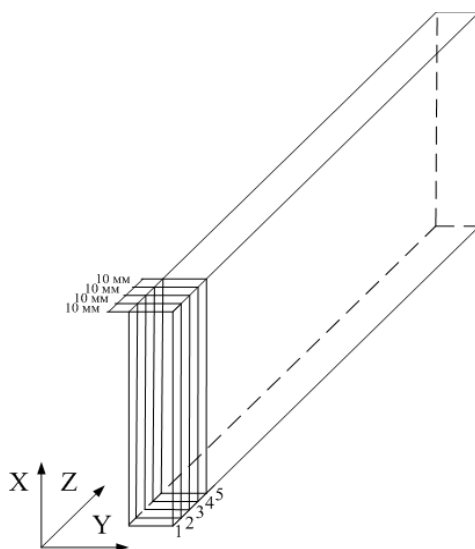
Сечения 1, 2, 3, 4 и 5 в заготовке с размерами 390 240 38 мм
